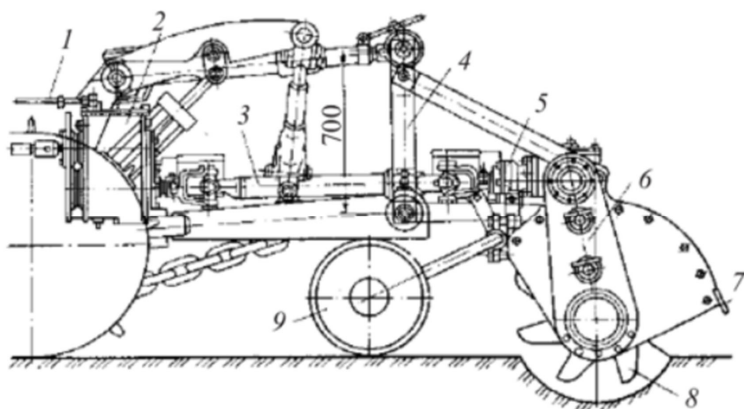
Фреза болотная навесная ФБН-2,0: 1,3 – карданный вал; 2, 5, 6 – редуктор; 4 – навеска; 7 – грабельная решетка; 8 – фрезерный барабан; 9 – опорное колесо.
